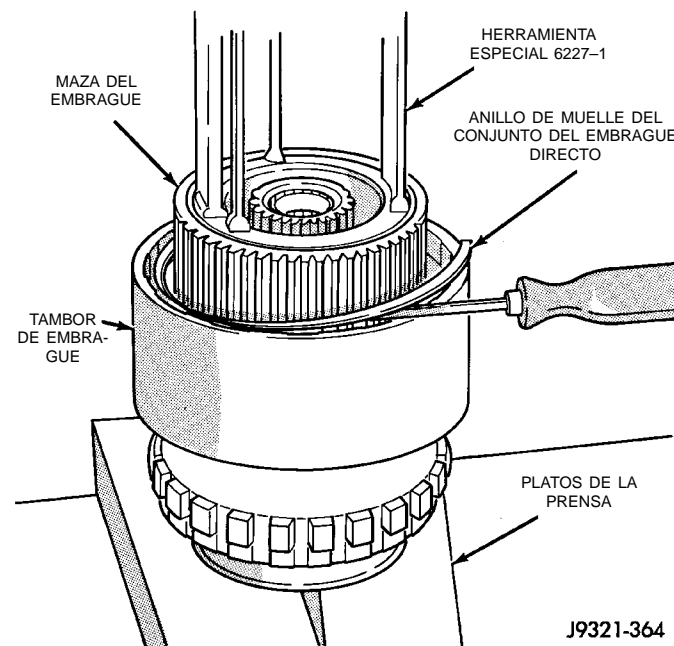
Desmontaje del anillo de muelle del conjunto del embrague directo
